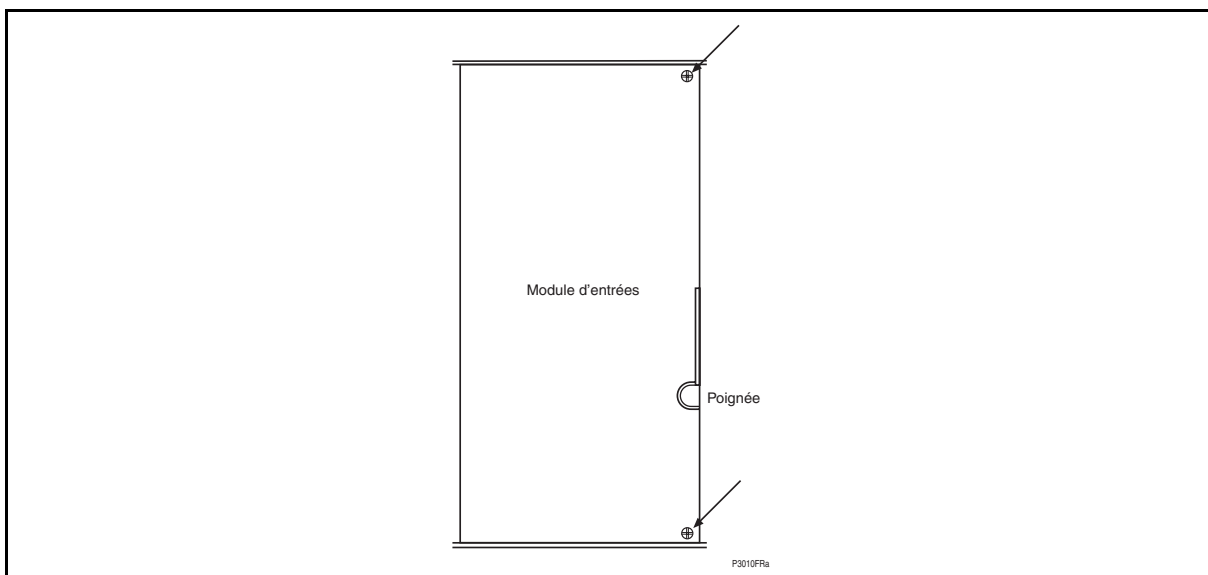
EMBLEMES DES VIS DE FIXATION DU MODULE D'ENTRÉE
